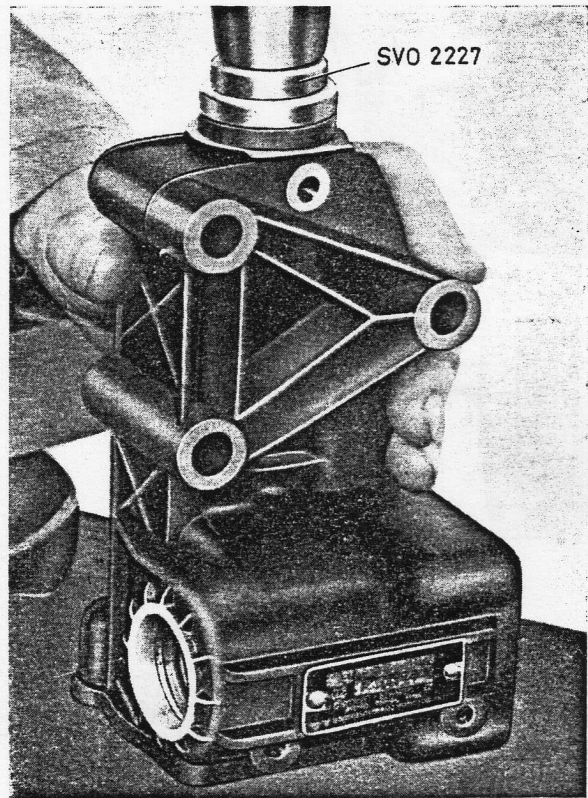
Radialdichtring für Lenkrollenwelle einpressen
